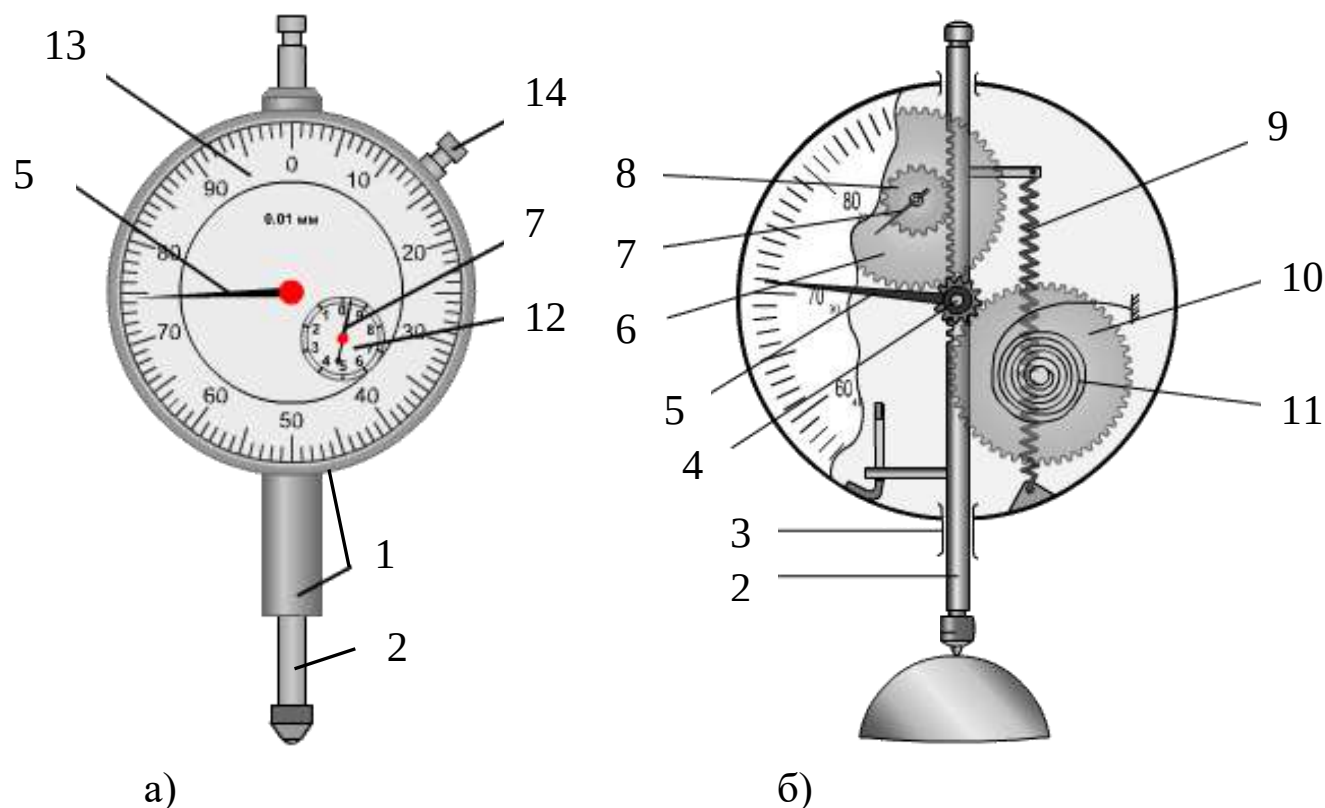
Індикатор годинникового типу: а) загальний вигляд; б) зубчаста передача
